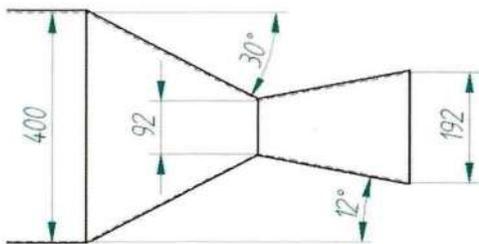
Dimensiones tobera del motor cohete de combustible sólido.
